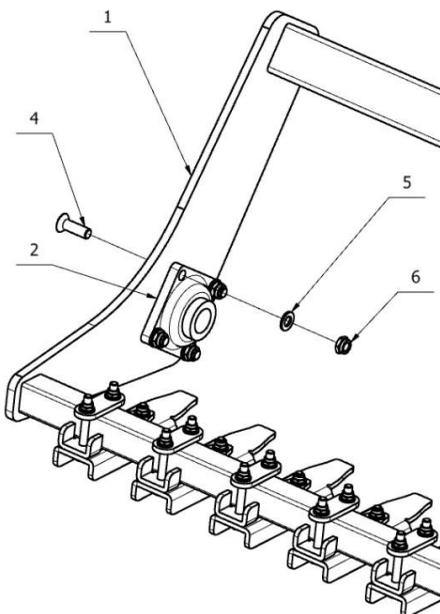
Dachwalze Plus Ø600mm auf Profil - Lagermontage.
